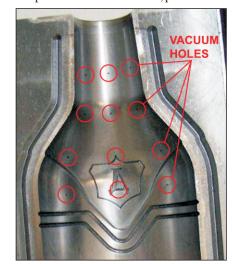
Stampo per il vetro con fori nella parte superiore (da Busellato Glass Moulds)
